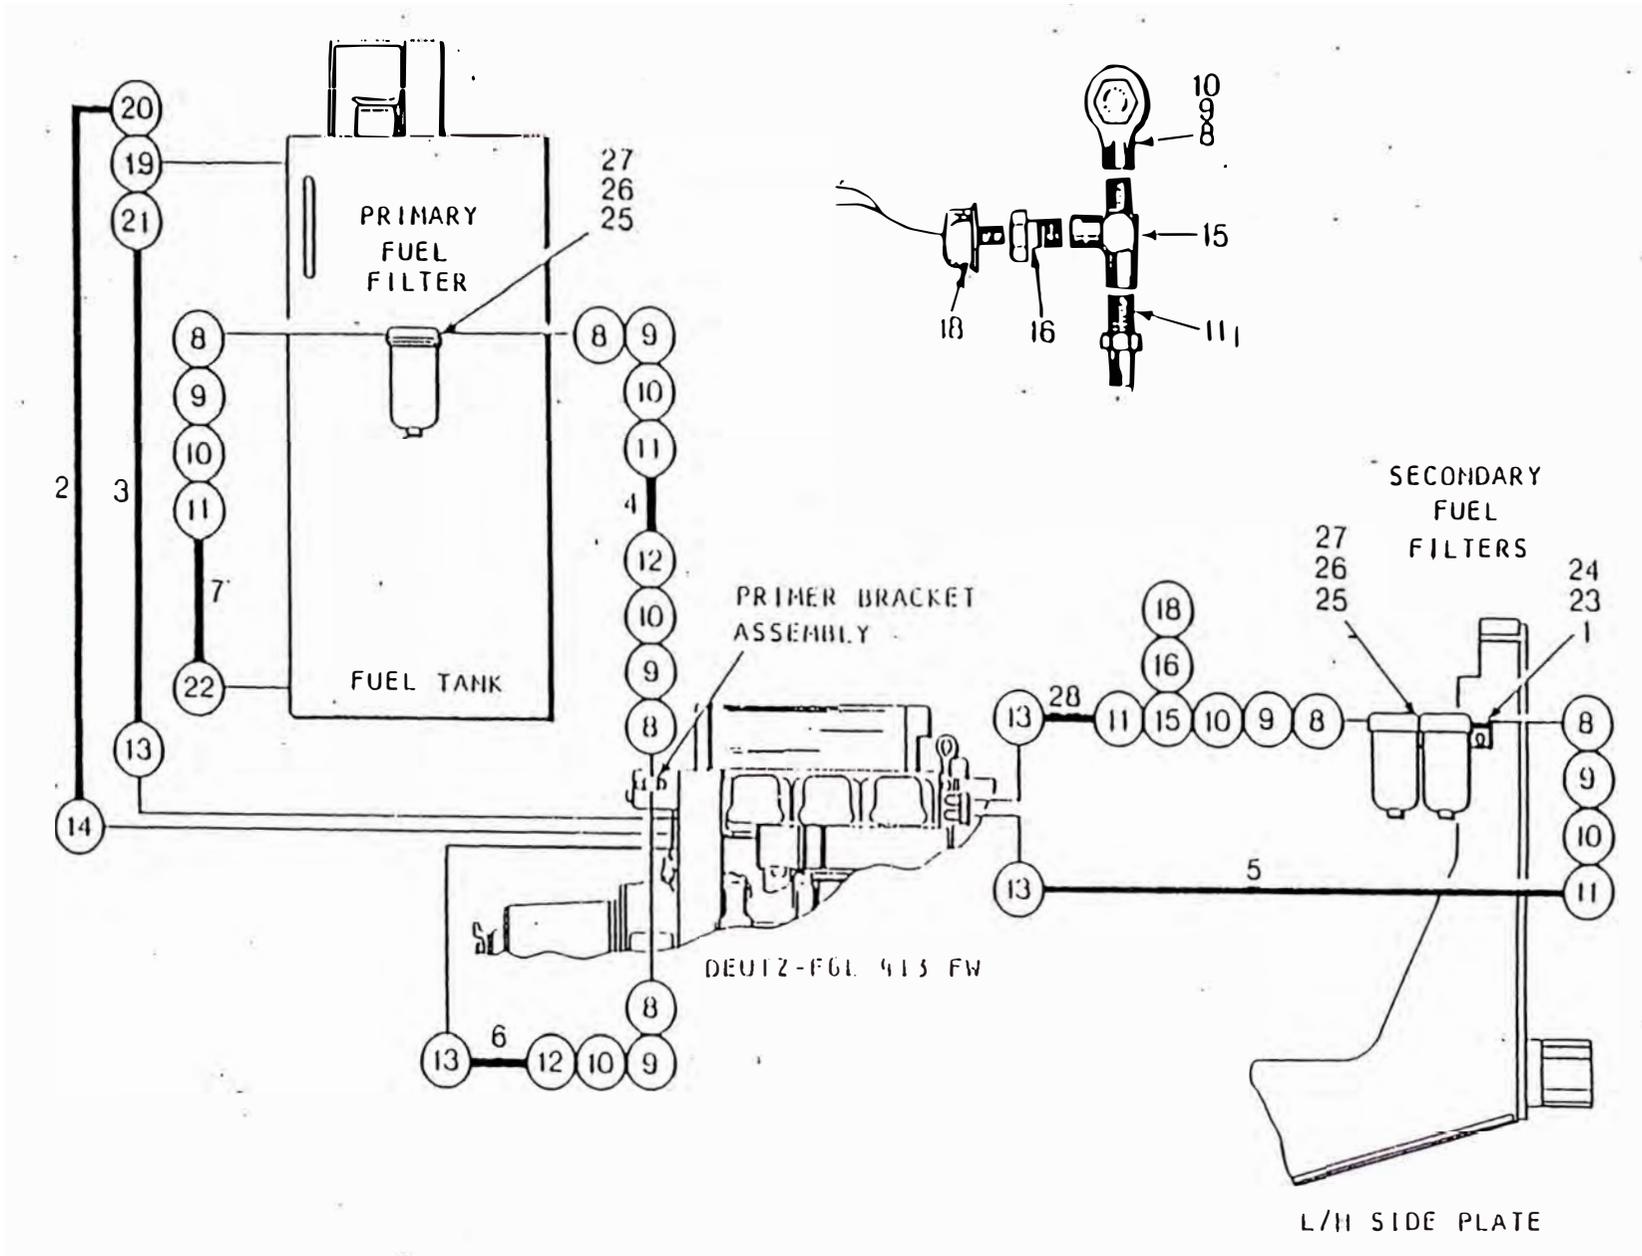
B SISTEMA DE COMBUSTIBLE
